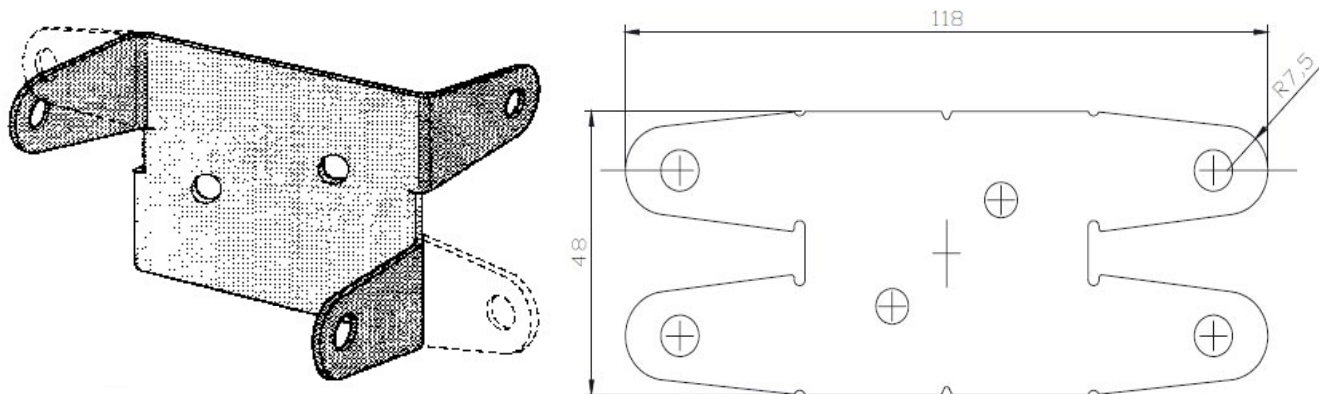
Croquis de perspective et vue en plan de la patte de liaison entre panneau
